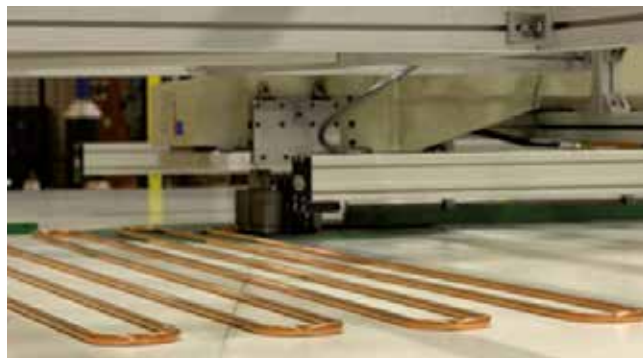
Hochpräzises Laserschweißverfahren.
